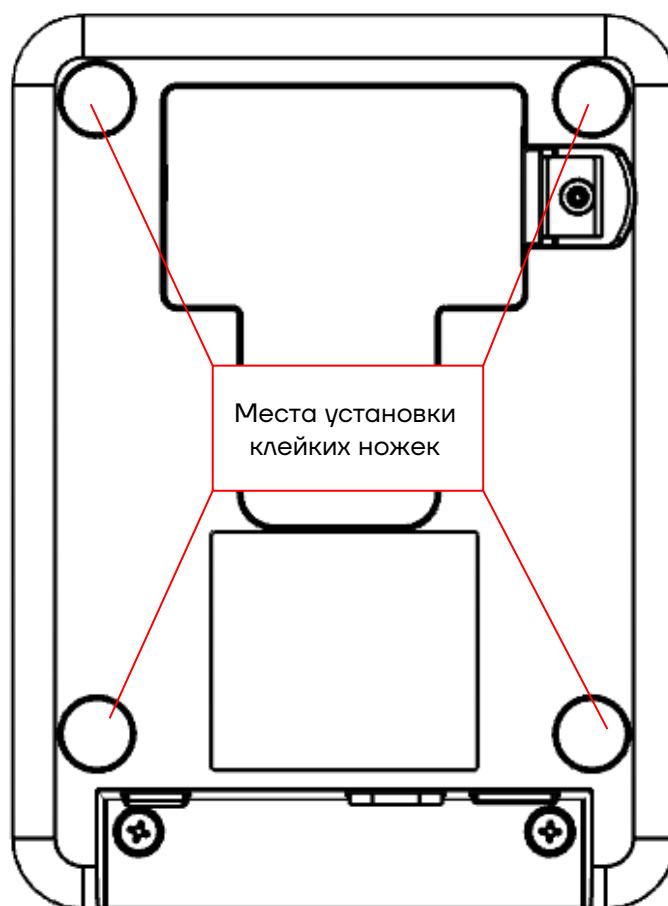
Места установки клейких ножек 3М 5501 D=10 h=1,6 в нижней части корпуса изделия
